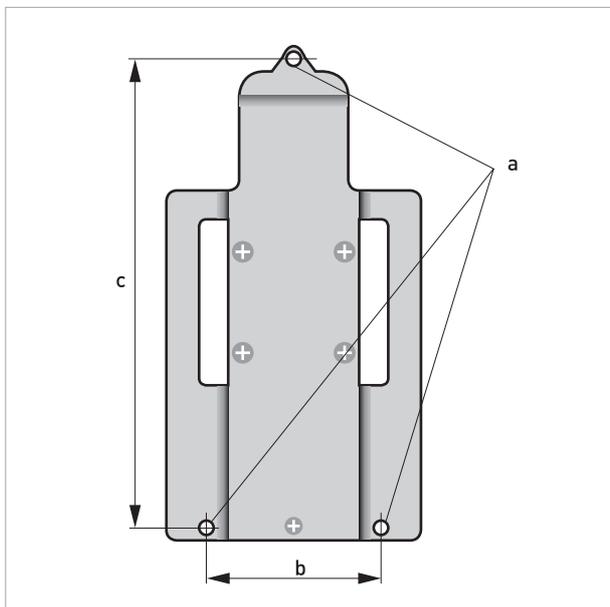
Размеры монтажной пластины корпуса для настенного монтажа из алюминия
